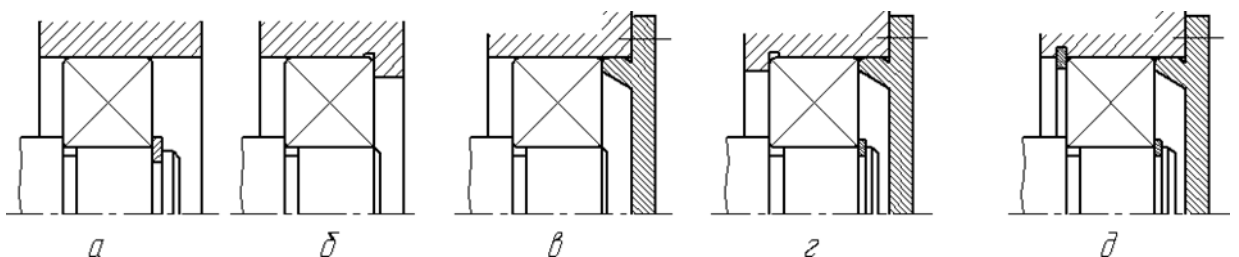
Кріплення підшипників кочення у корпусі опори
